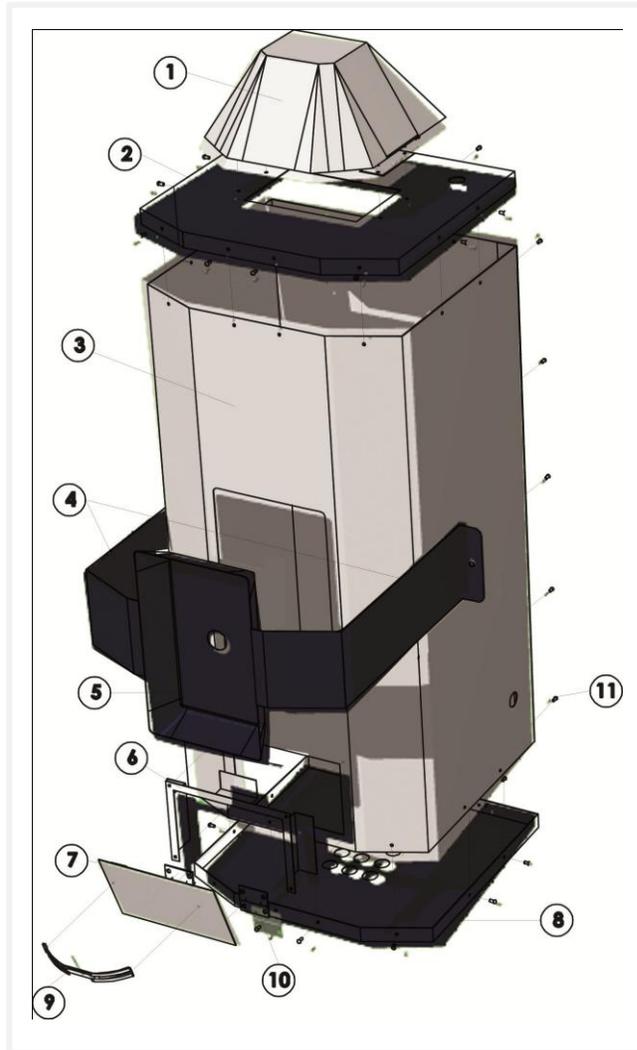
Explosivo del modelo de carcasa para calentador de agua (PL-01).
